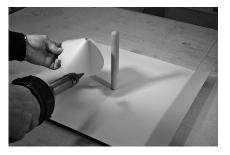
Разогревают внутреннюю и внешнюю кромки конуса.
